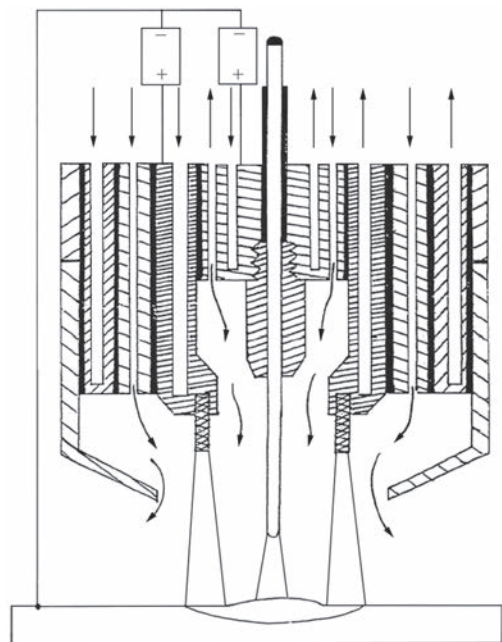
Гибридная горелка для сварки плавящимся и неплавящимся электродами с коаксиальной подачей проволоки сквозь кольцевой катод
